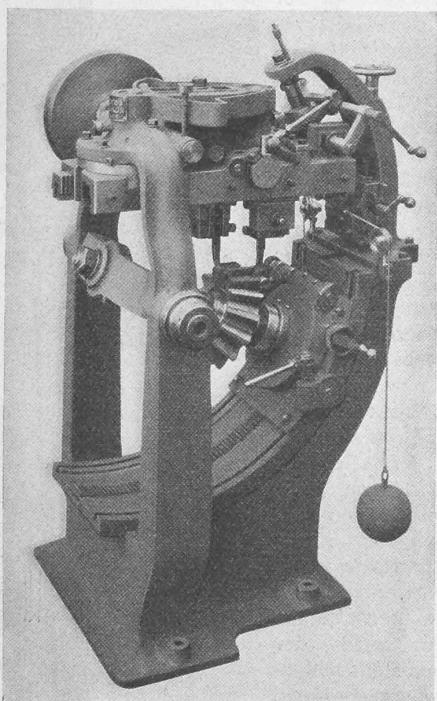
Räderhobelmaschine für Kegelräder bis 500 mm Durchmesser.
